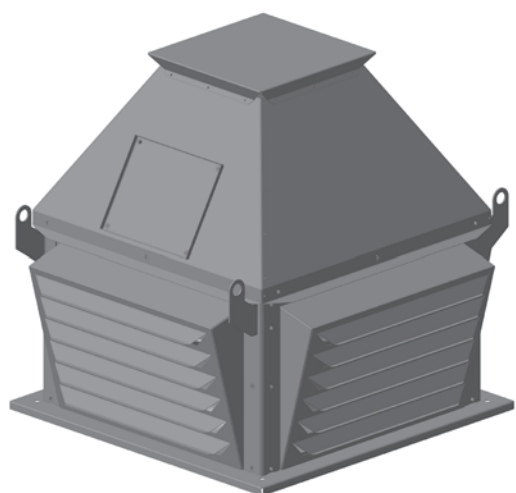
Установка вентилятора крышного радиального на монтажный стакан.
